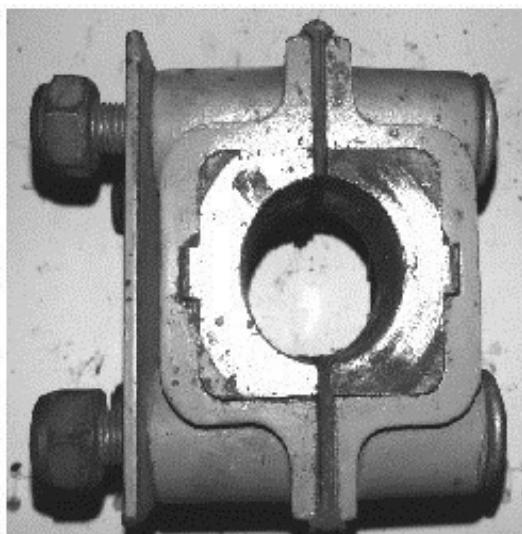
Подшипниковый узел коленчатого вала соломотряса комбайна Енисей-1200, смазанный консистентной смазкой
